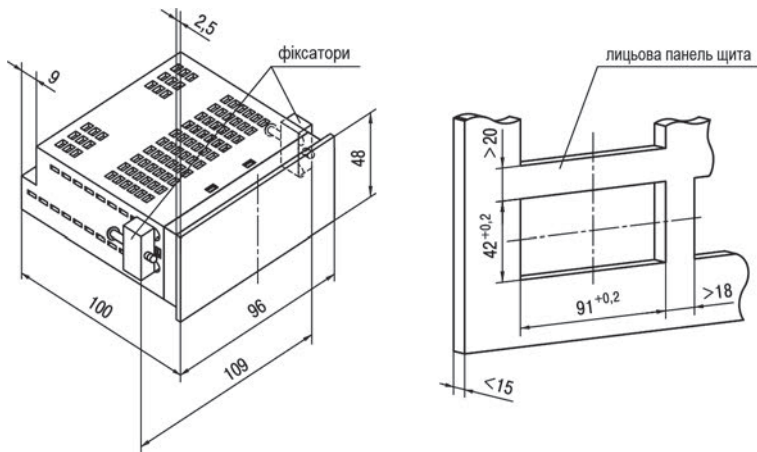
Пристрій щитового кріплення у корпусі типу Щ2
